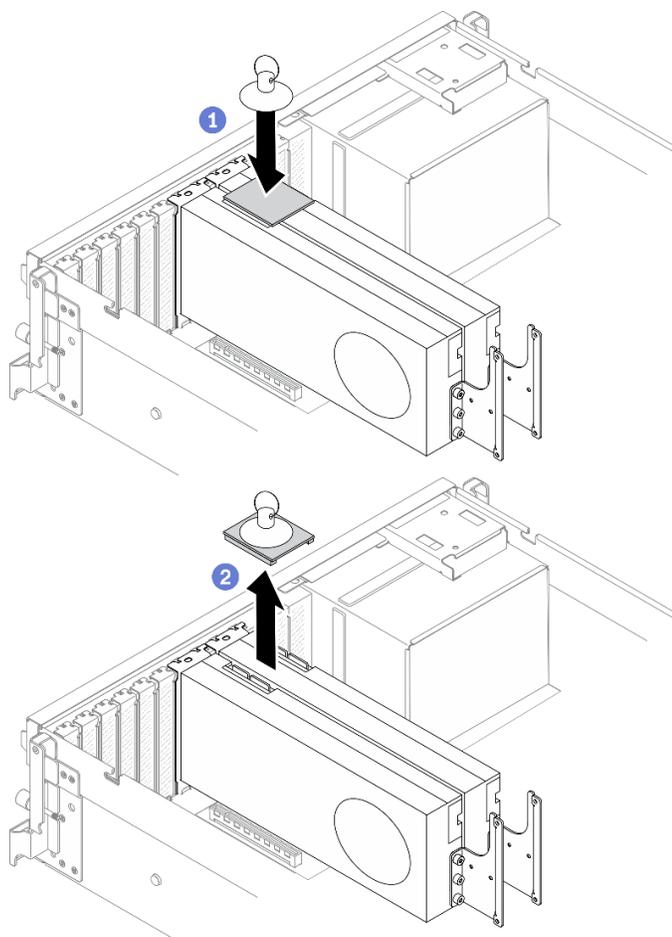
Rimozione del Bridge di collegamento dell'adattatore GPU
